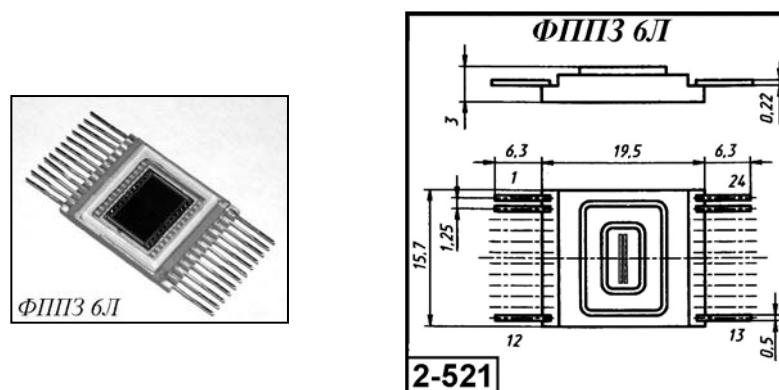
Внешний вид и габаритные размеры ФППЗ 6Л
